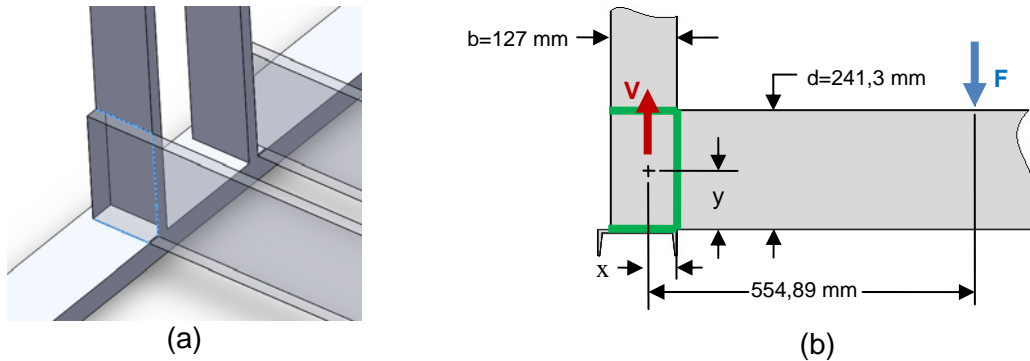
Juntas soldadas sob torção: arestas de solda (a) e vista frontal (b).
